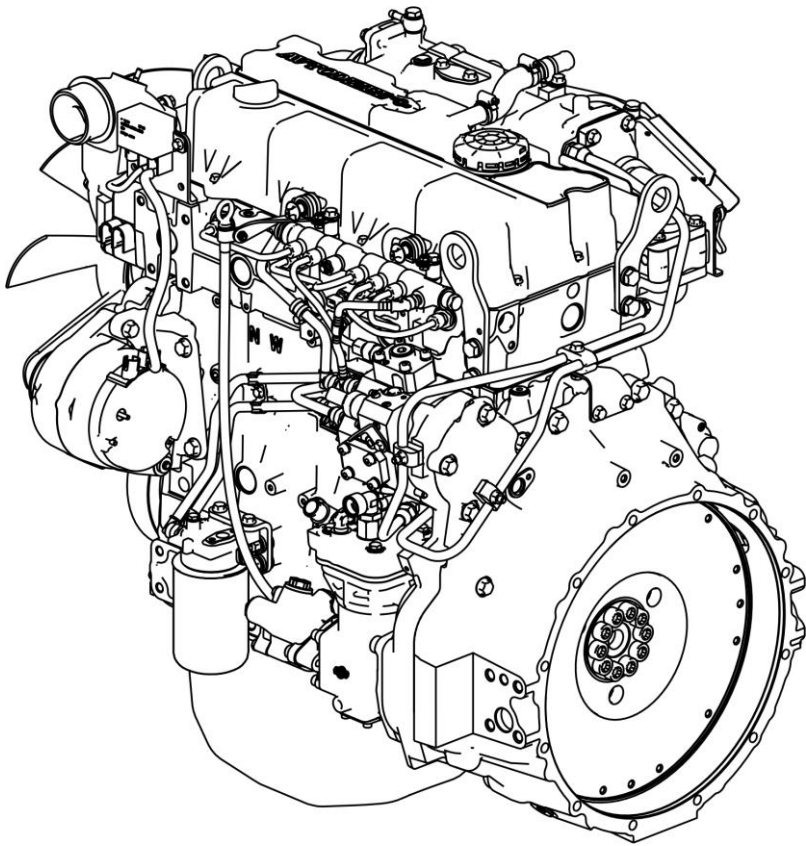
а – Двигатель ЯМЗ-53443-21 (общий вид слева)
